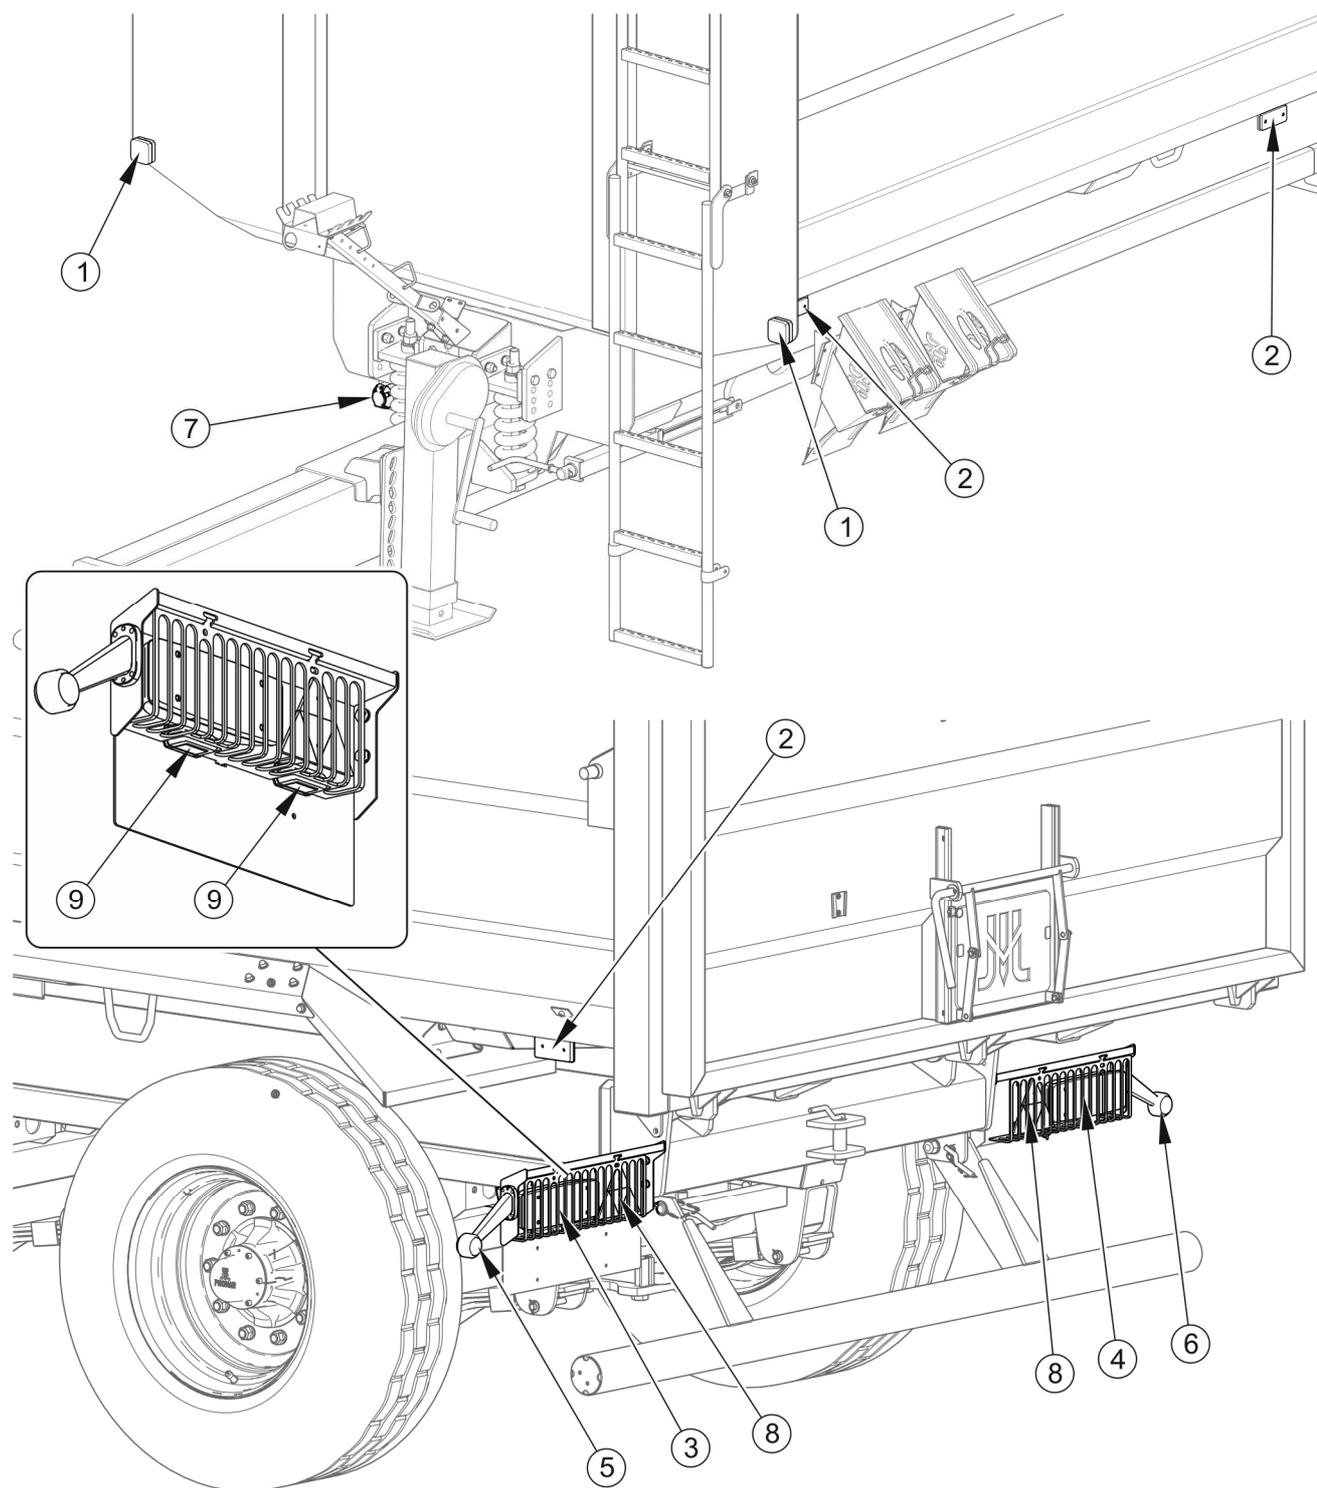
Layout dei componenti elettrici e riflettenti
